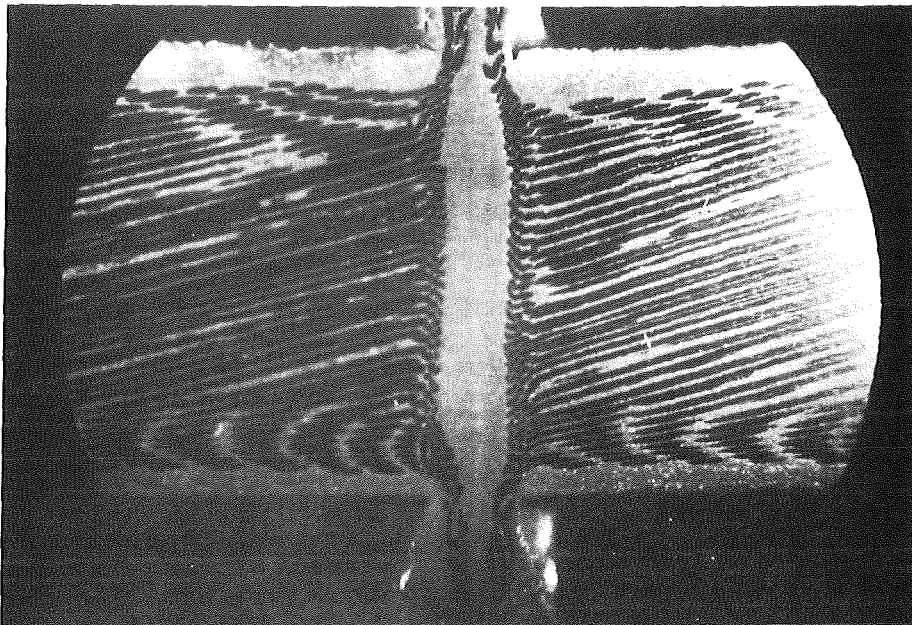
a) Längsschnitt durch eine Kaltpreß-Schweißstelle.
